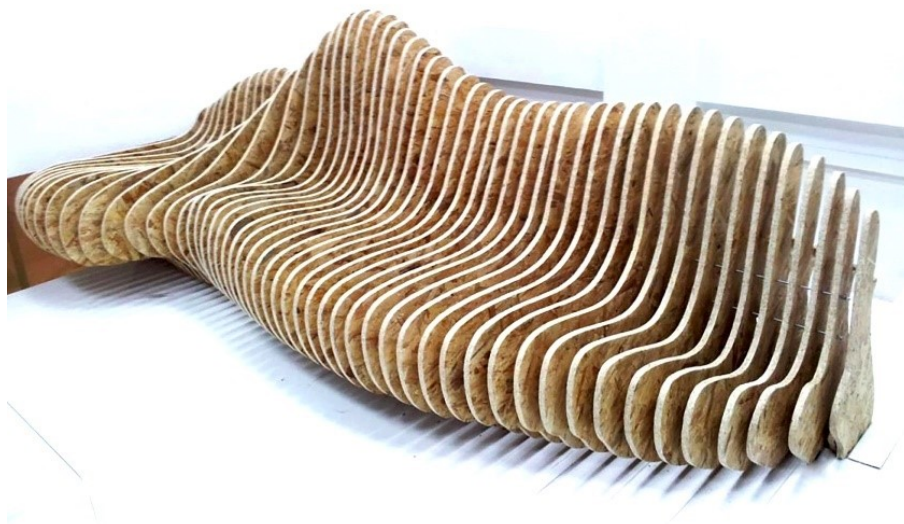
Imagen del banco y barandilla, donde se puede observar detalladamente el banco, acompañado de unas barandillas metálicas, para poder unir todas las piezas. Fuente: [Benacci \(2020\)](#)
